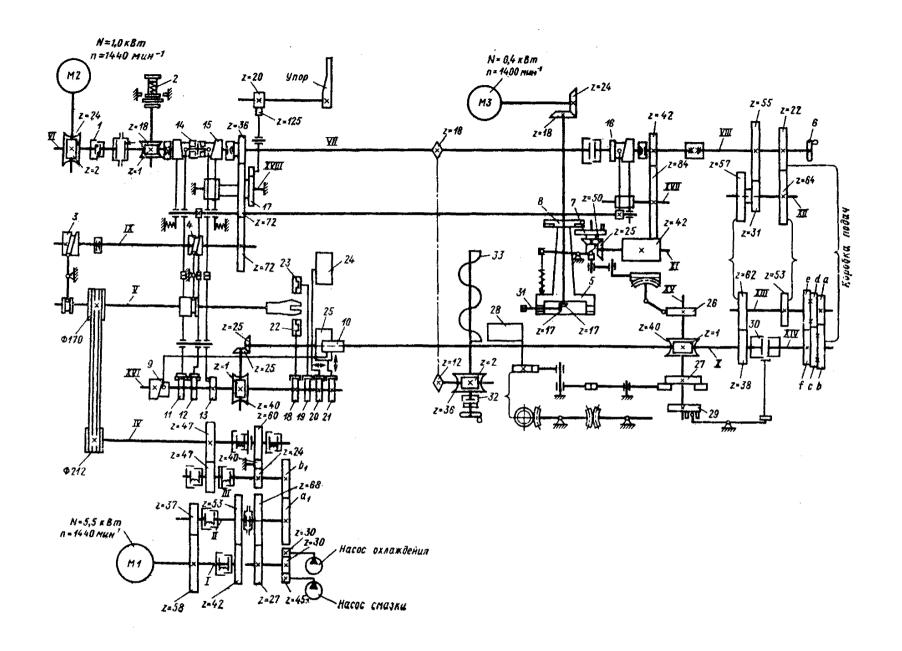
Кинематическая схема токарно-револьверного автомата 1Б140
